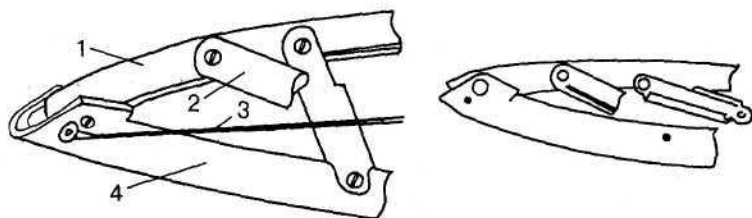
Стыковка штевневых окончаний с откидным пиллерсом: 1 — мидельвейс; 2 — привальный брус; 3 — опорный трюсик; 4 — штевень
